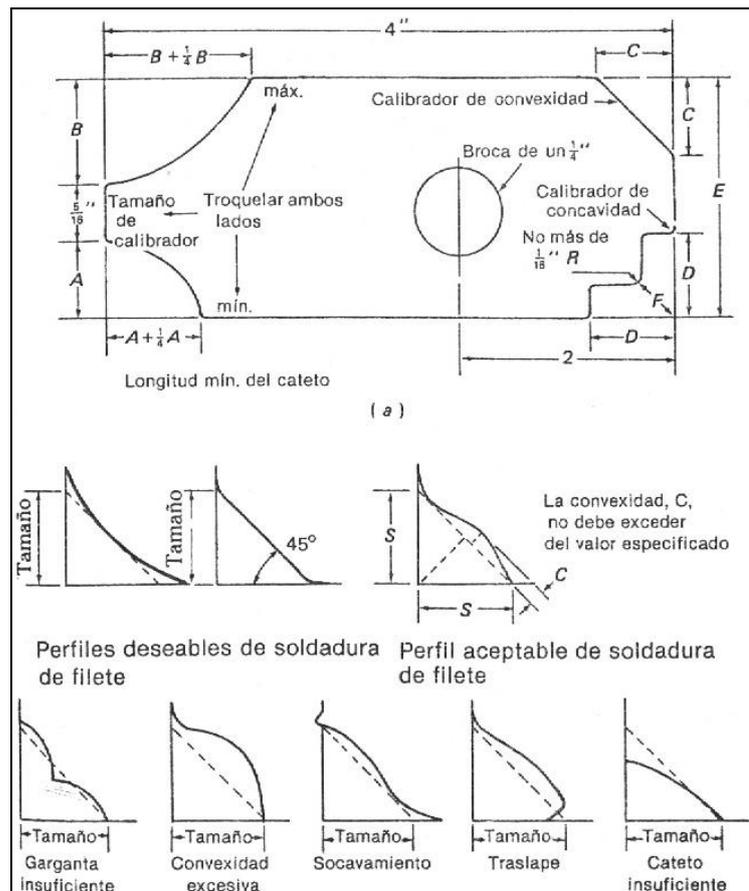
a) calibrador de soldaduras para cordones de filete únicamente. Abajo, perfiles aceptables y defectuosos de soldaduras de filete
